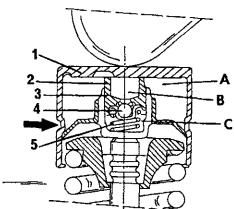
Разрез гидравлического толкателя (16клапанный двигатель). Ссылки на цифровые и буквенные обозначения приводятся в тексте.
